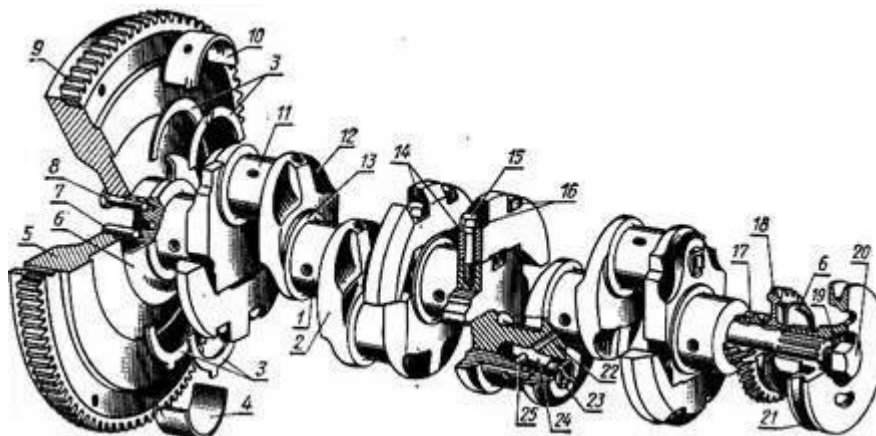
Колінчастий вал дизеля: 1- корінна шийка; 2, 12 – щоки; 3- упорні півкільця; 4 – нижній вкладиш корінного підшипника; 5 – маховик 6 - масловідбивна шайба; 7 – установочний штифт; 8 – болт; 9 – зубчатий вінець; 10 - верхній вкладиш п'ятого корінного підшипника; 11 – шатунна шийка; 13 – галтель; 14 – противага; 15 – болт кріплення противаги; 16 – замкова шайба; 17 – шестерня колінчастого вала; 18 – шестерня приводу масляного насоса; 19 – упорна шайба; 20 – болт; 21 – шків; 22 – канал підведення масла в порожнину шатунної шийки; 23 пробка; 24 – порожнина в шатунній шийці; 25 – трубка для чистого масла
